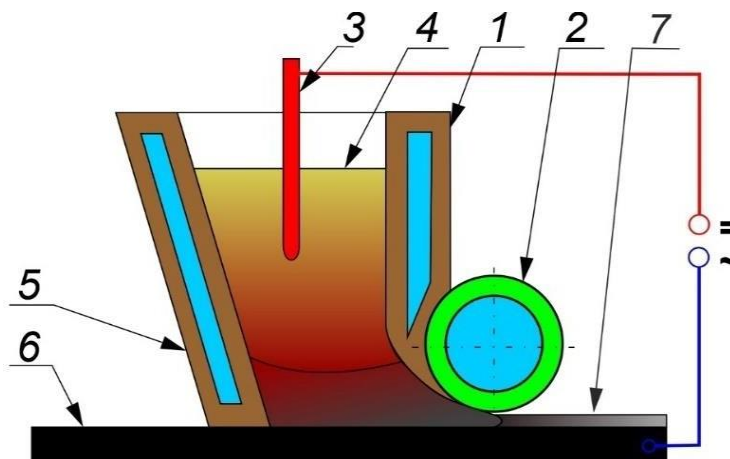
Схема здійснення процесу горизонтальної електрошлакового наплавлення плоскої поверхні [66]: 1 – кокіль–кристалізатор; 2 – валок–кристалізатор; 3 – наплавочний дріт; 4 – шлакова ванна; 5 – металева ванна; 6 – наплавлений метал
